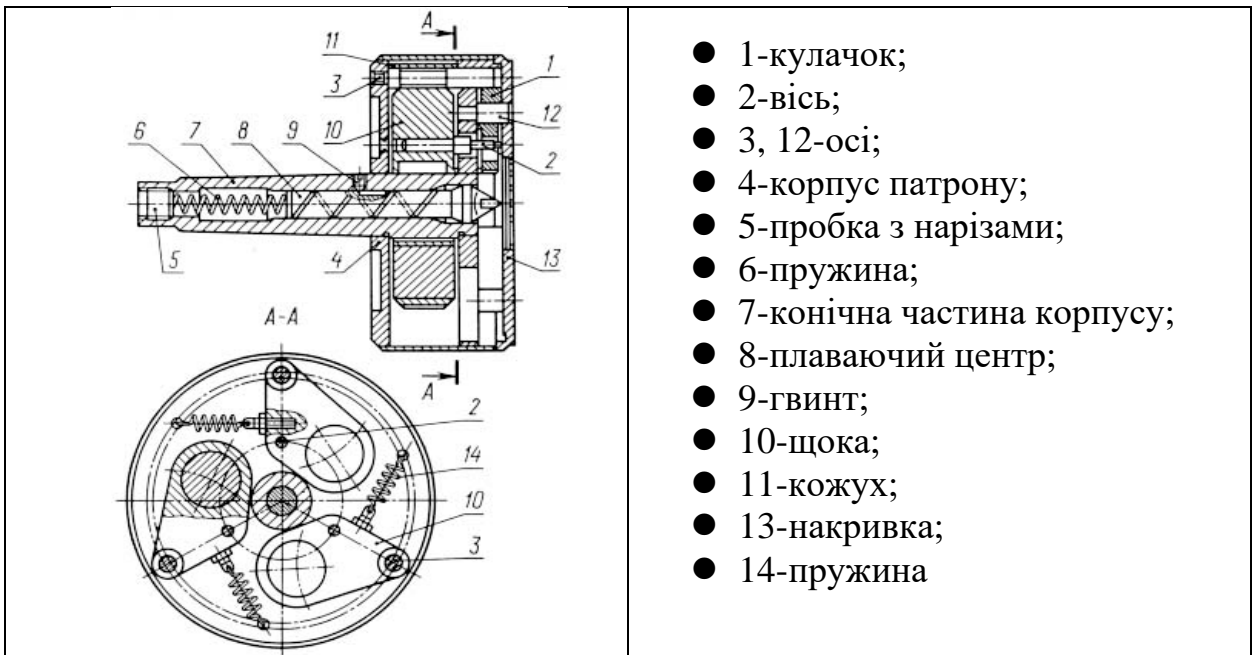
Універсальний трикулачковий повідковий патрон для базування деталей в центрах
